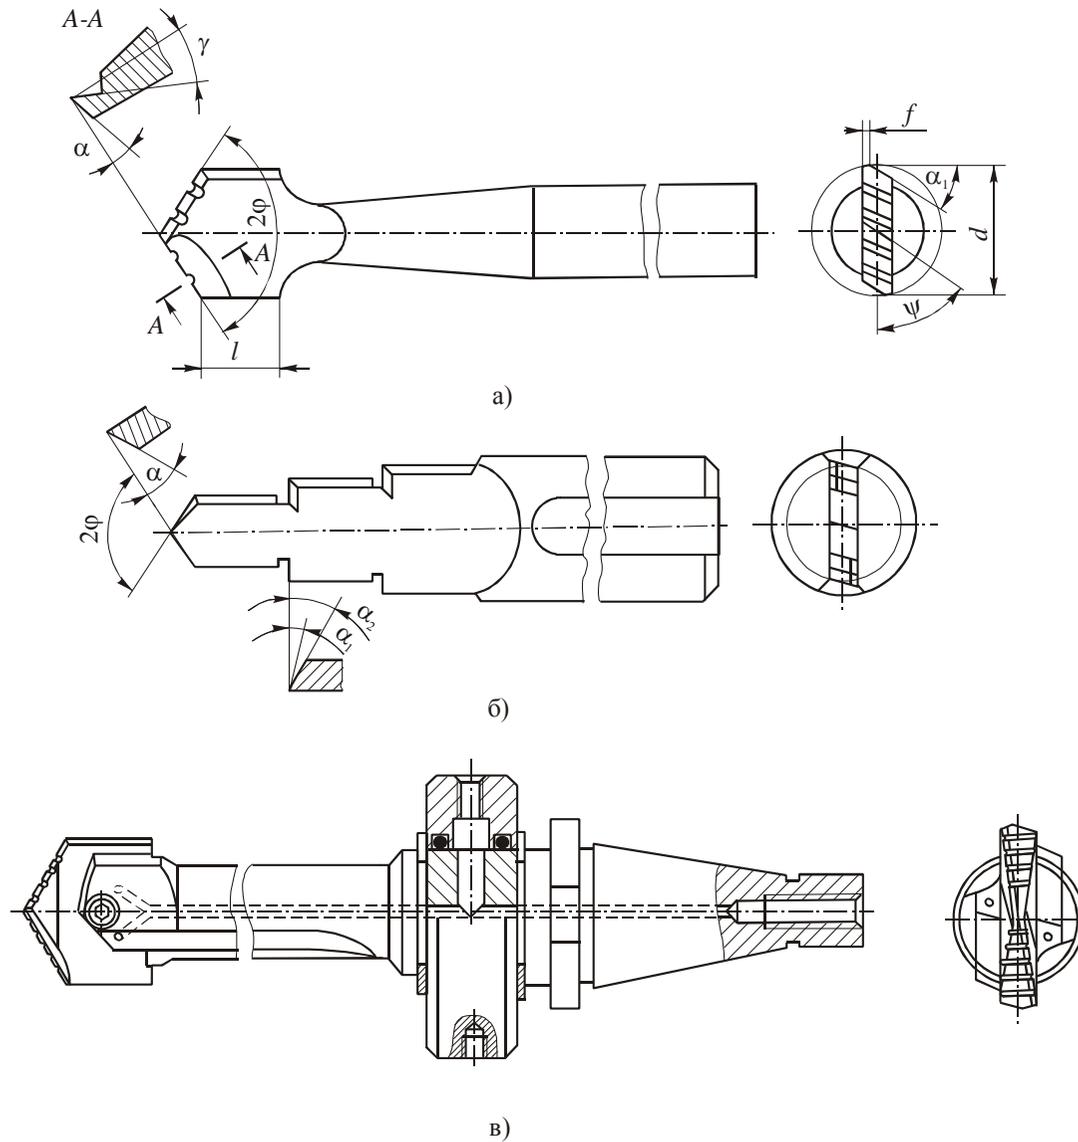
Перовые сверла: *a* – цельное; *б* – для сверления ступенчатых отверстий; *в* – сборное, с внутренним напорным охлаждением
